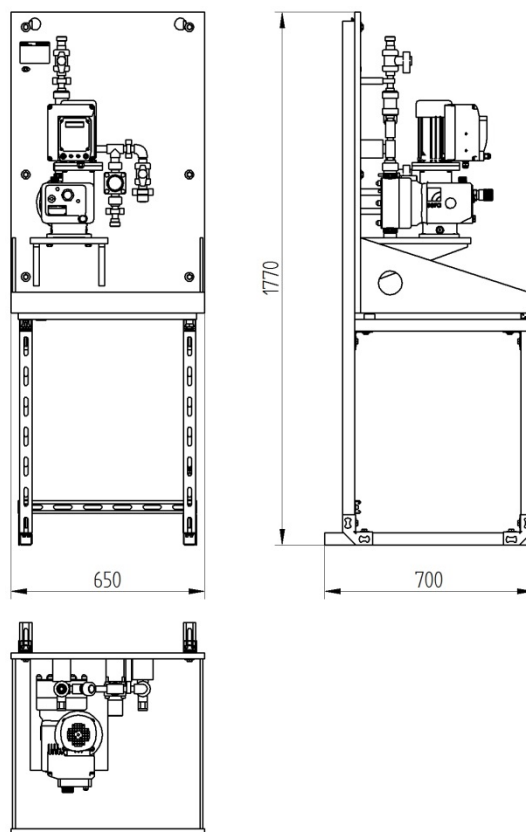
Dimensions CVD 1s (montage au sol, châssis acier)
